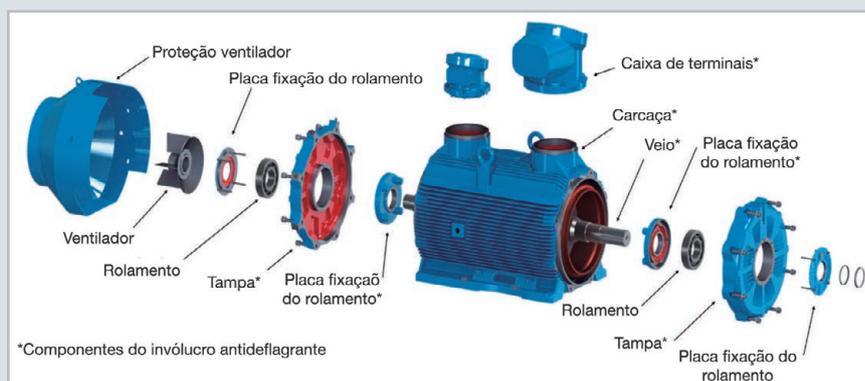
Vista explodida de um motor elétrico assíncrono trifásico.
